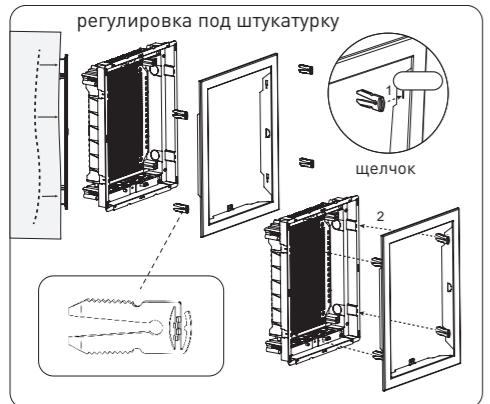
Установка 4-х защелок для крепления и регулировки двери по глубине.
